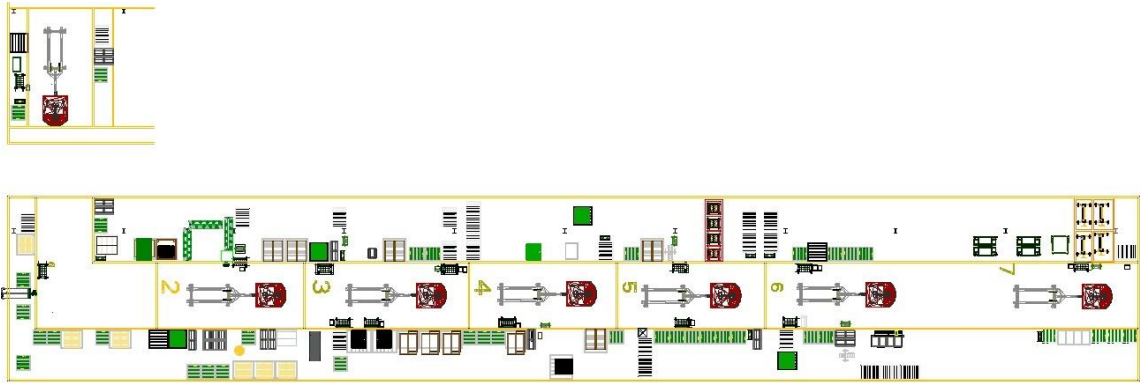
Layout en AutoCAD 3D de la línea de chasis.
